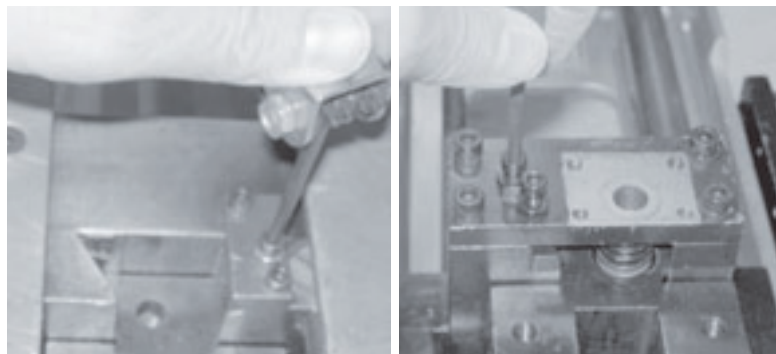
Para ajustar la tensión del portaherramientas, retraiga el tornillo de ajuste posterior (izquierdo), luego atornille los tornillos de ajuste frontal.
